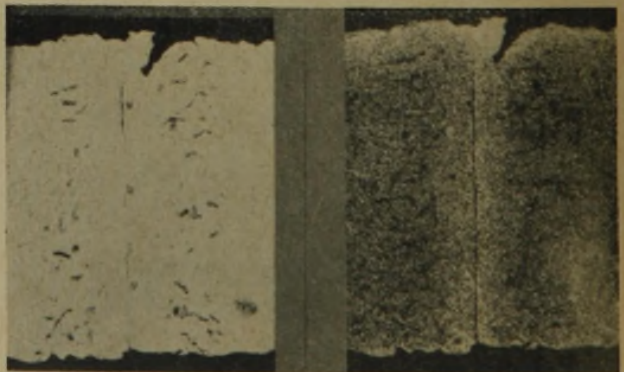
Elektro-Stumpfschweißung aus Speisewasser-Vorwärmer
